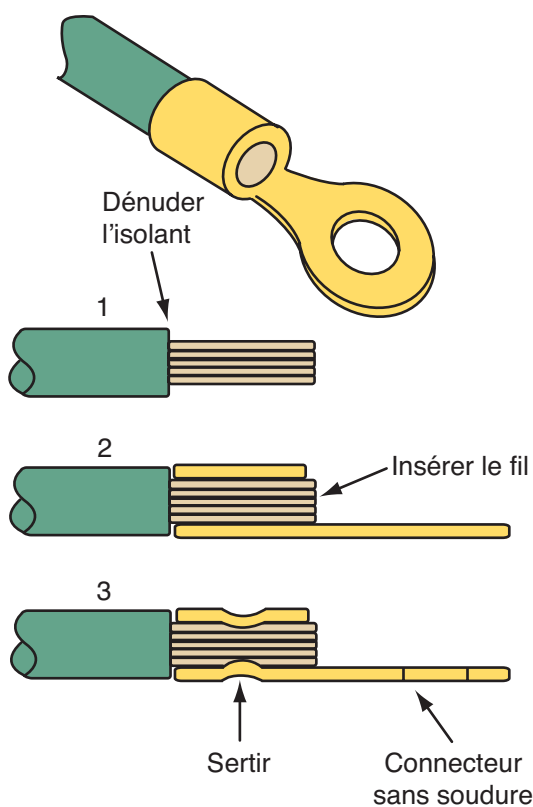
Installation et sertissage d'un connecteur sans soudure.
